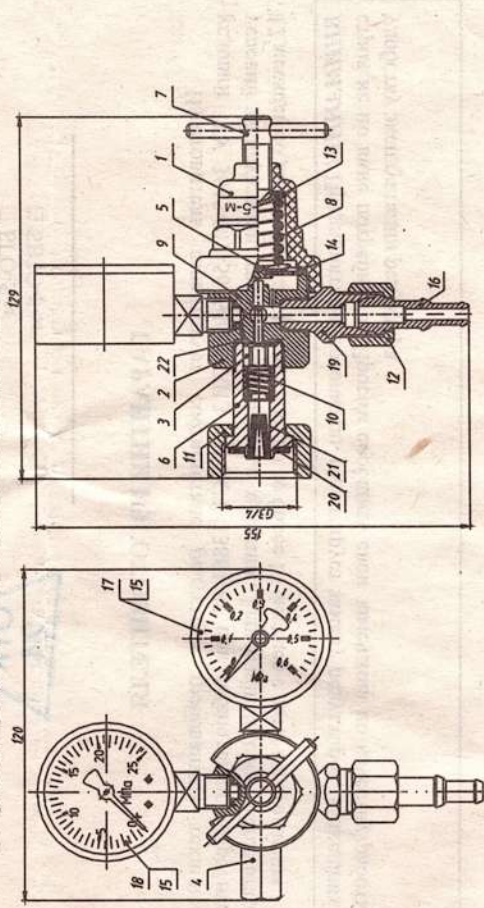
Редуктор баллонный газовый одноступенчатый.
